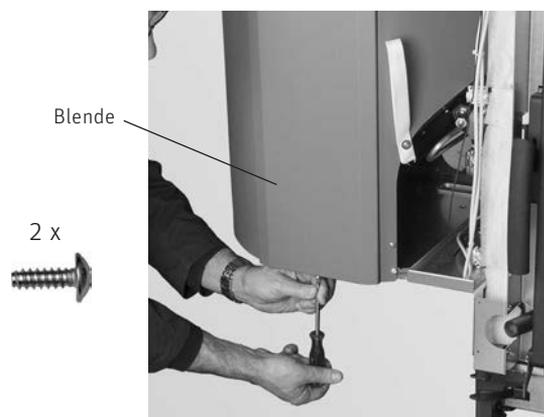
Blende aufstecken und mit 1 Blechschraube befestigen
